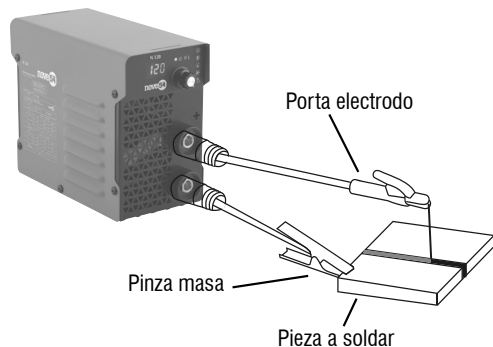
Montaje de los cables de soldadura para soldar Electrodo Recubierto (MMA)
